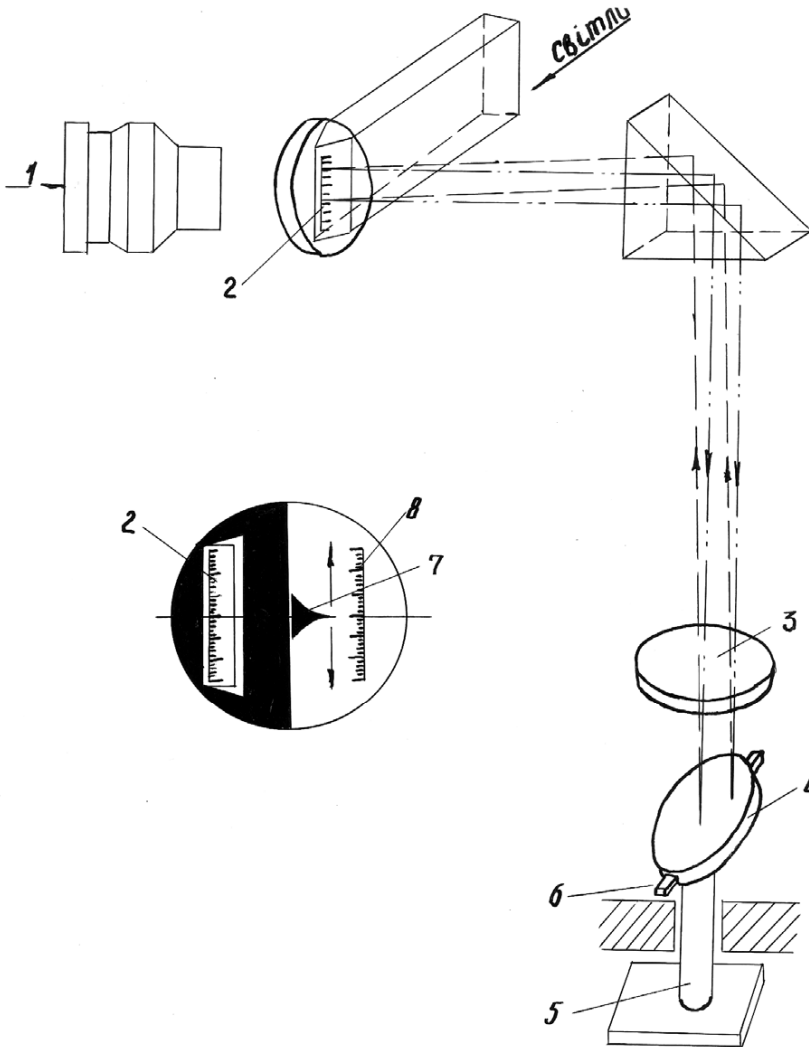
Оптична схема оптиметра: 1 – окуляр; 2 – шкала; 3 – об’єктив; 4 – дзеркало; 5 – вимірювальний штифт; 6 – опора; 7 – показчик; 8 – відбита шкала
